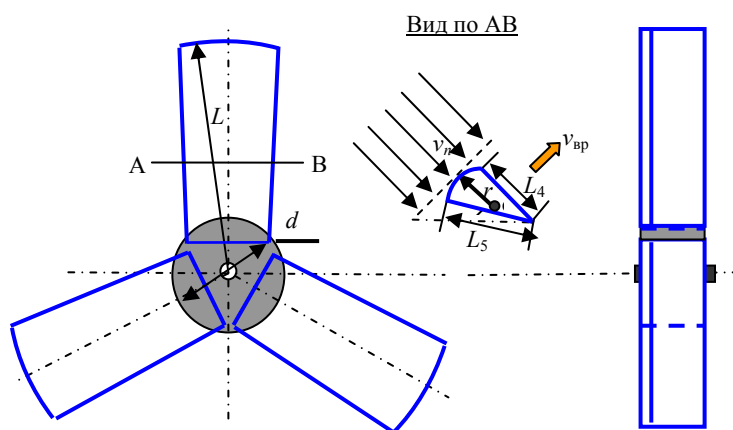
Общий вид расположения лопастей в винте и их поперечный разрез
